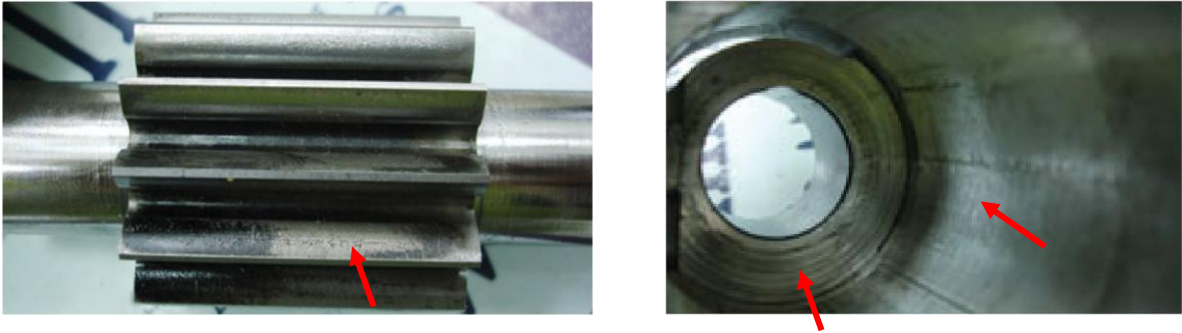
Desgaste abrasivo numa bomba de engrenagens.
